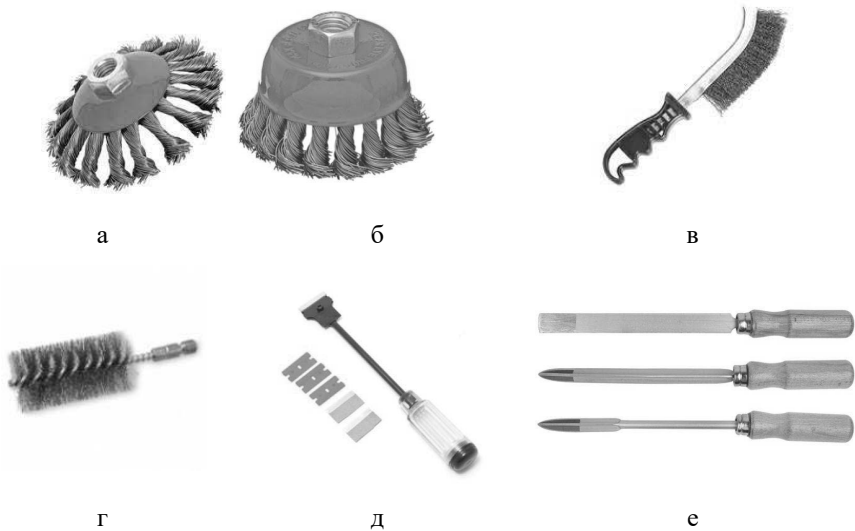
Інструмент для механічного та ручного очищення поверхонь:
